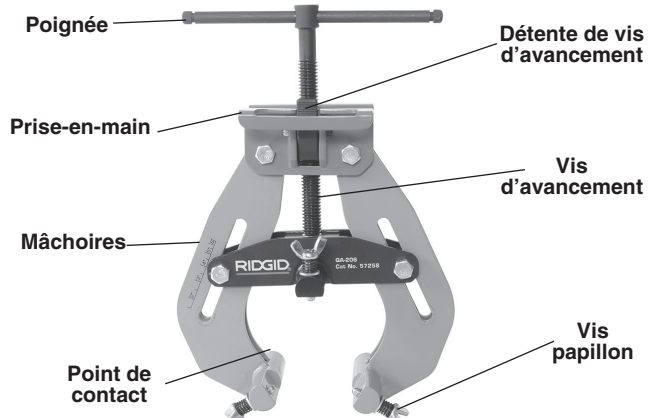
Pince de soudage rapide pour tuyaux
